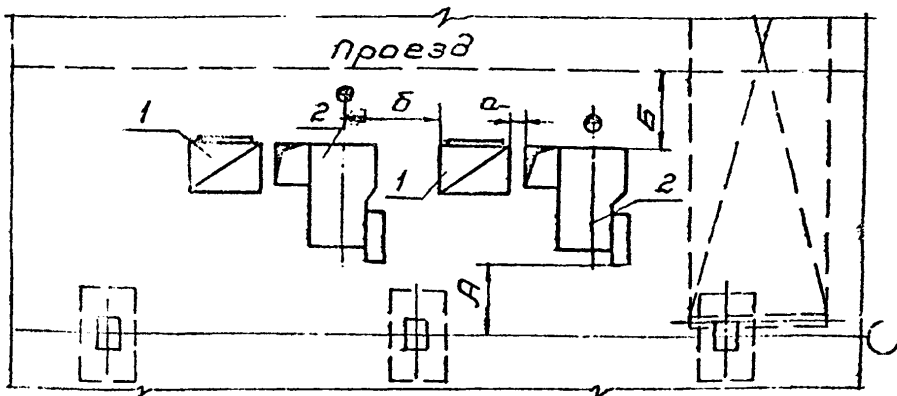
Схема расположения штамповочных линий на базе ГКМ:
